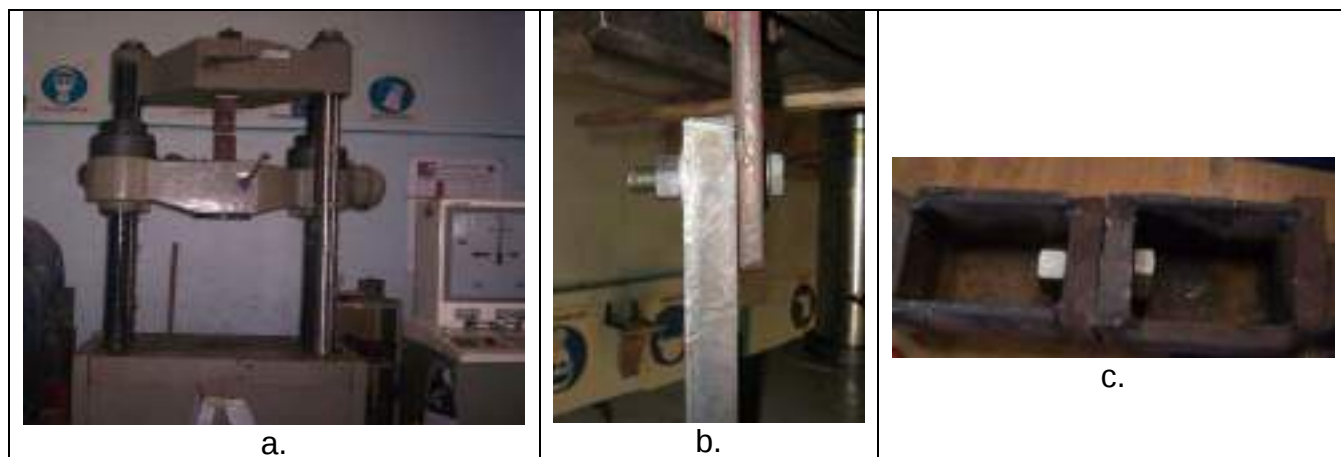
Ensayos en los tornillos. a) Máquina de ensayos. b) Montaje de ensayo de corte. c) Montaje de ensayo de tensión
